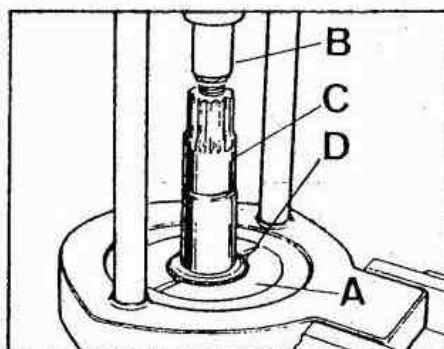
Desmontaje del cojinete de cabeza del piñón de ataque
